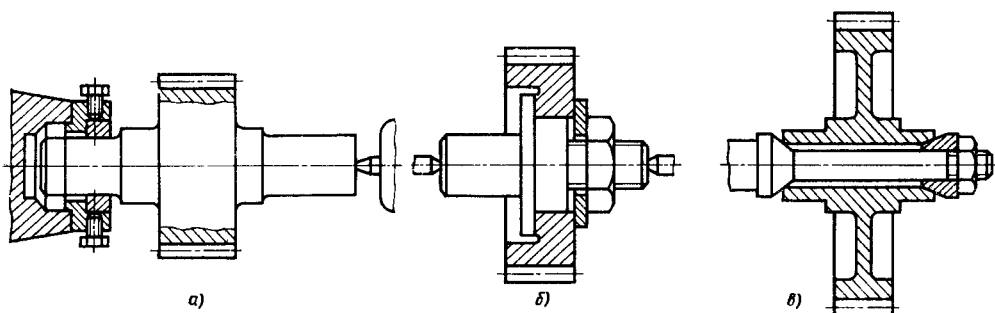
Схемы установки заготовок зубчатых колес на зубошлифовальном станке с горизонтальной осью заготовки:
